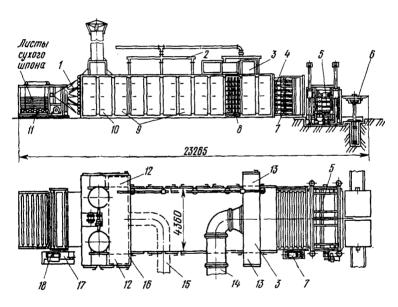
Общий вид газовсй роликовой сушилки СРГ-25: 1— разгрузочное устройство, 2— паровые трубы системы пожаротушения, 3— распределительный канал, 4— загрузочная этажерка, 5— загрузочный механизм, 6— подъемные платформы, 7— колонка натяжения цепей, 8— приводные ролики, 9— секции сушки, 10— секции охлаждения, 11— роликовый стол, 12, 13— боковые каналы, 14— газоход подачи газа в камеру, 15. 16— подъемные газоходы подачи отработавшего газа в камеру смешения, 17— коробка скоростей, 18— лебедка
